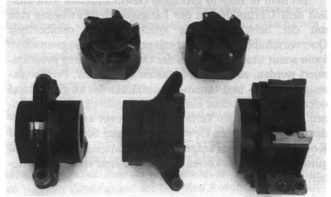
Fräsbohr-Werkzeuge zum Vollbohren und Auskammern (Heller, Bremen)
